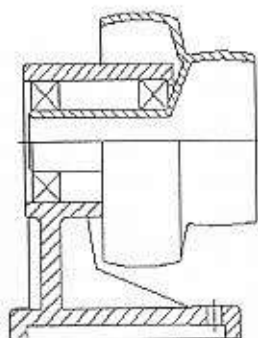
Varijanta sa min. vremenom zamene kaiševa
